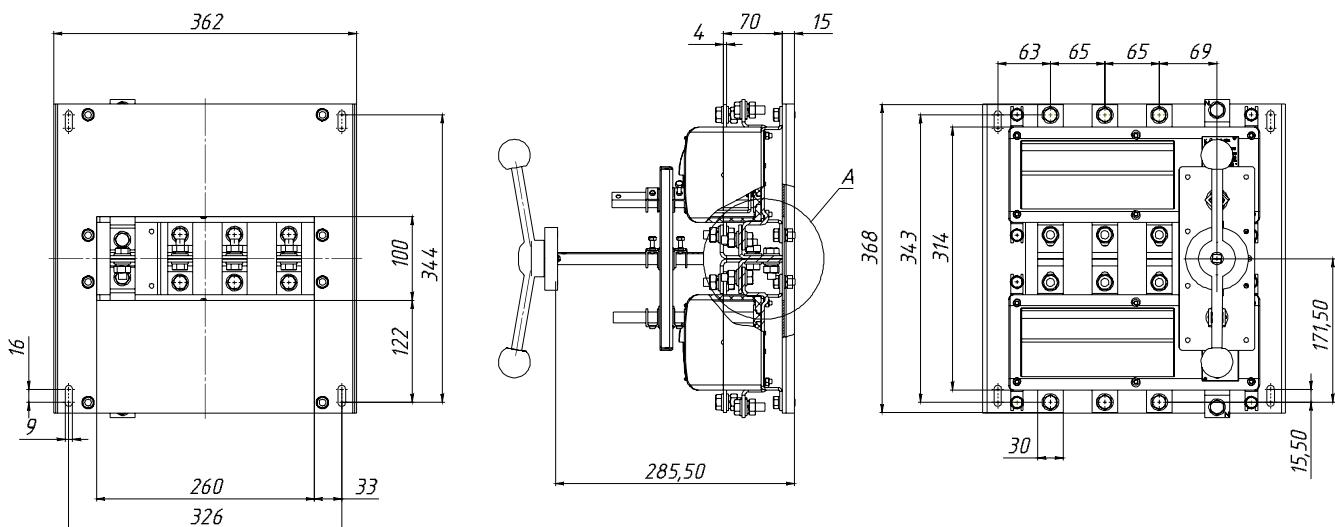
Выключатель-разъединитель ВНК-35-31130-32 УХЛЗ
